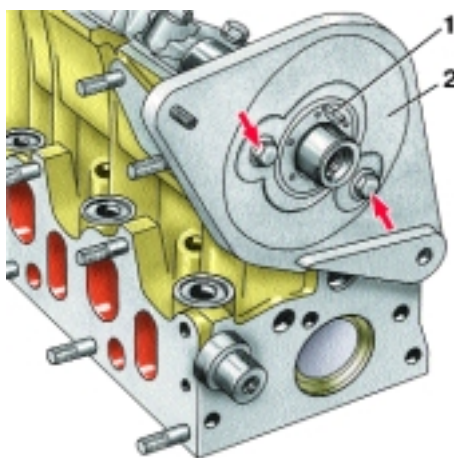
Снятие заднего кожуха ремня привода ГРМ двигателя F3R 272: 1 – шпонка; 2 – задний кожух
